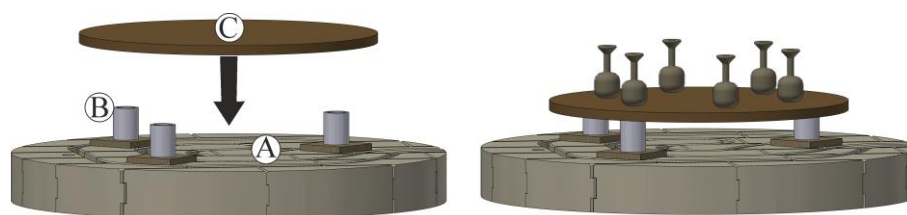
Colocar a placa (C) sobre as colunas (semelhante à figura)
